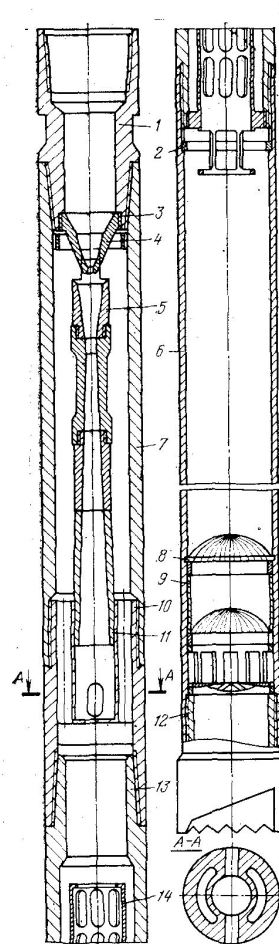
Металлоулавливатель Е. М. Курнева и Н. И. Лукинова:
